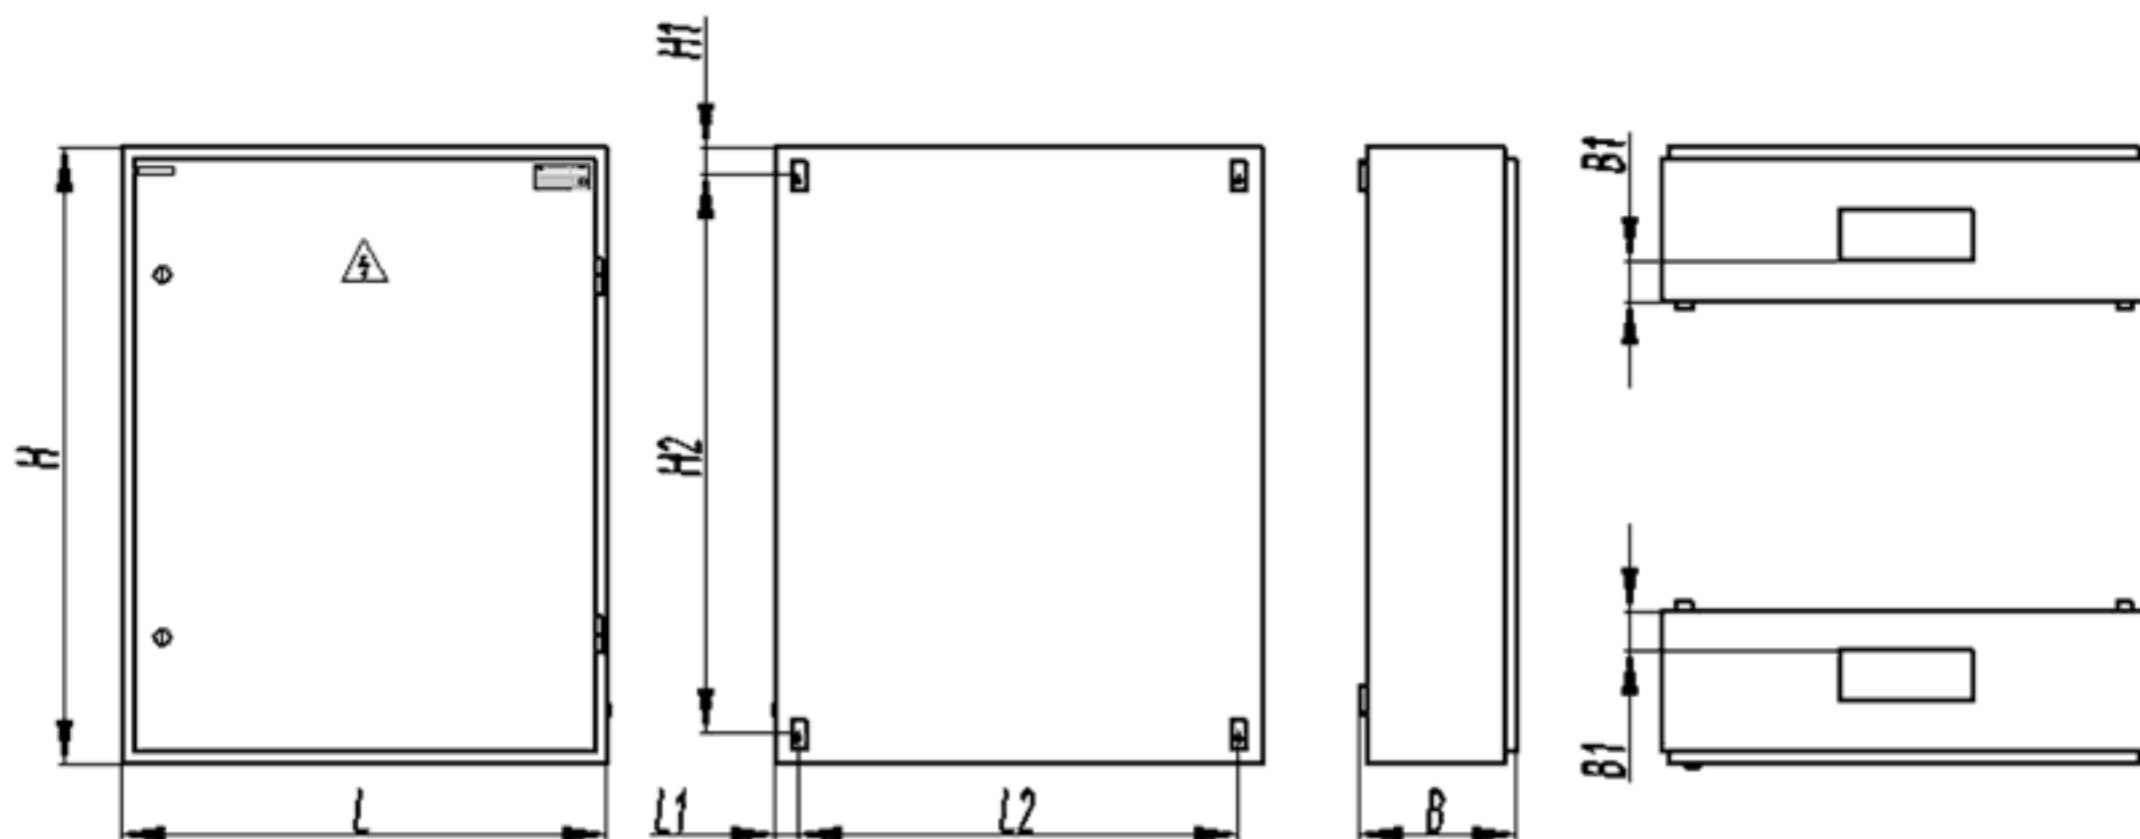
(Схема разметки отверстий для монтажа щитка типа ЩРВ).
